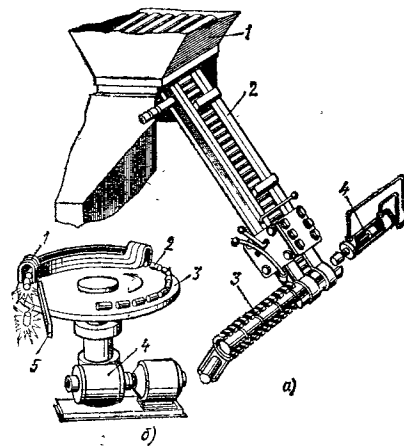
Методические индукционные установки для нагрева мерных цилиндрических заготовок:
